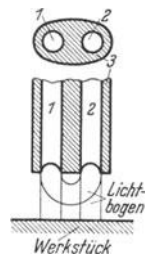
Grundform der Drehstromlichtbogenschweißung.
